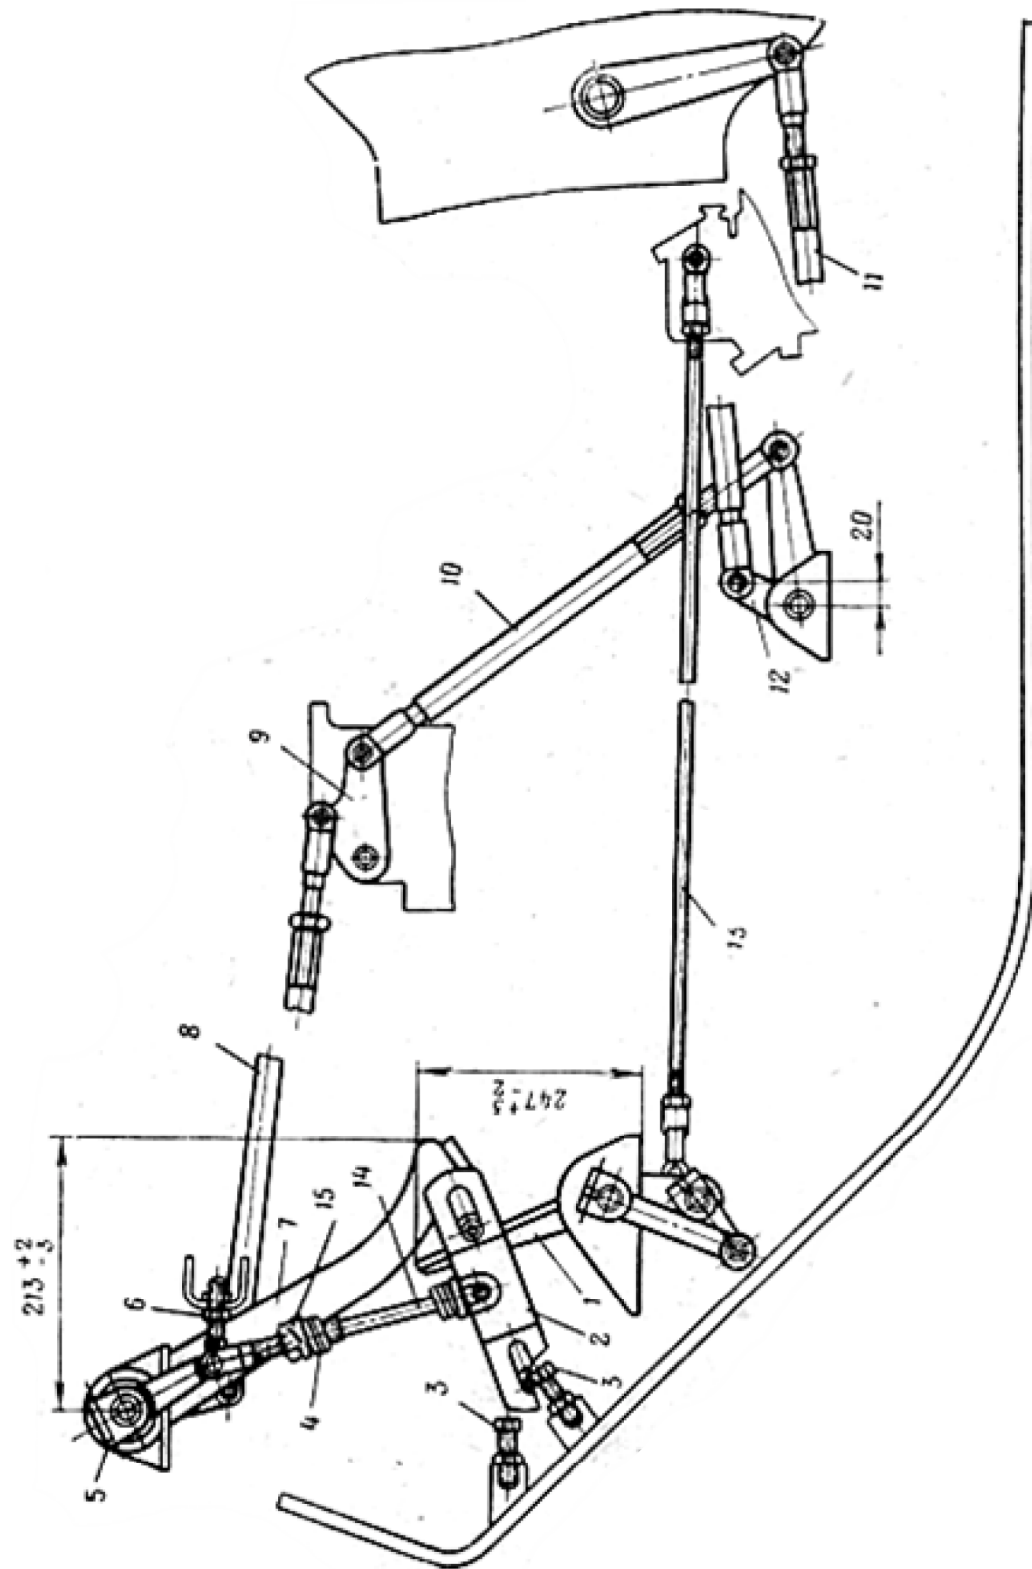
Схема регулировки педали главного фрикциона и педали остановочного тормоза транспортера-тягача МТ-Л:
